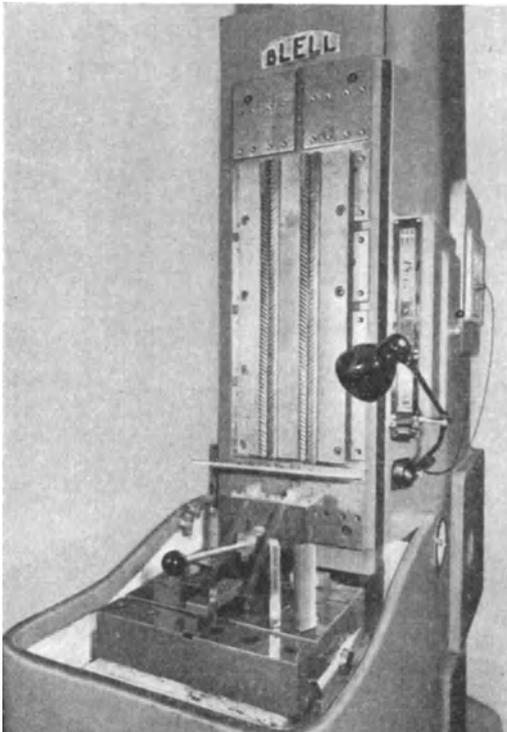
Werkzeugschlitten einer senkrechten Räummaschine (Blell); Räumzeug und Räumvorrichtung (Schilling).
